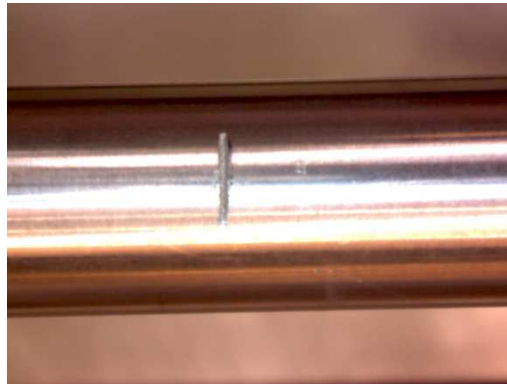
Eje fisurado al 16% de su diámetro.
